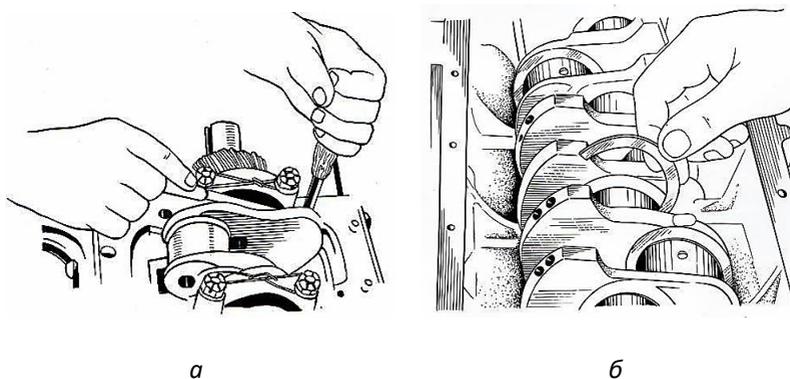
Проверка осевого люфта коленчатого вала щупом (а) и установка упорных полуколец КВ в гнезда среднего коренного подшипника
